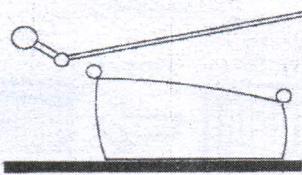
Откидывание руля машины с поднятием опорного вала.
